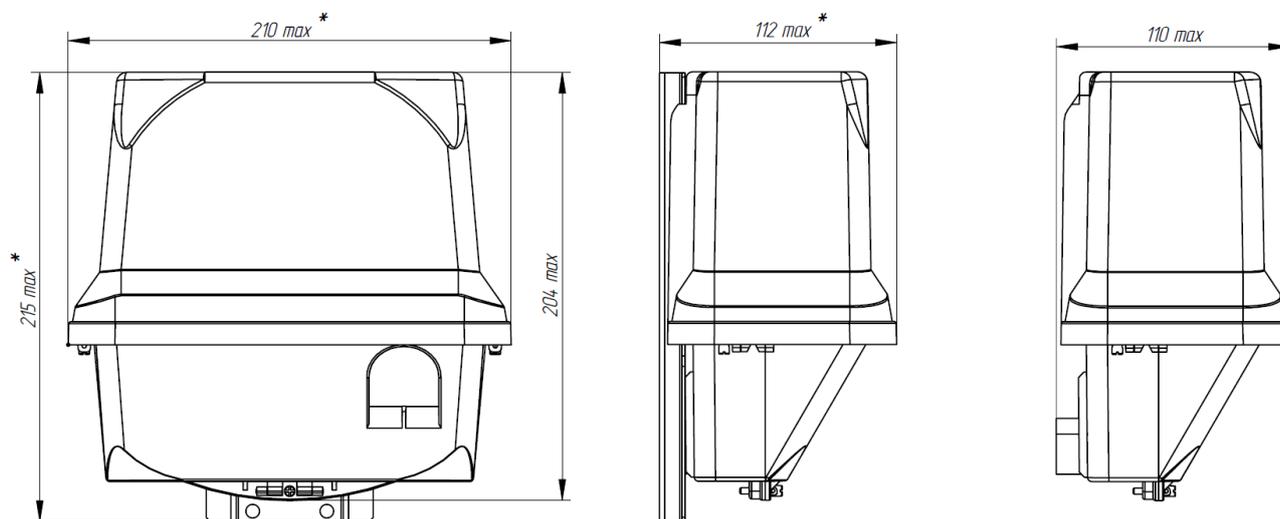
Корпус SPLIT (измерительный блок, * габаритные размеры)
